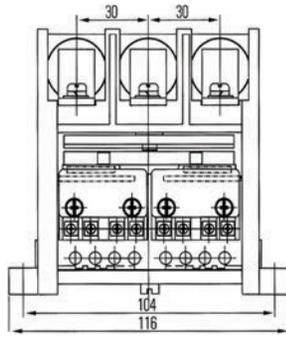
Габаритные размеры КВТ-1,14-80/125/160
